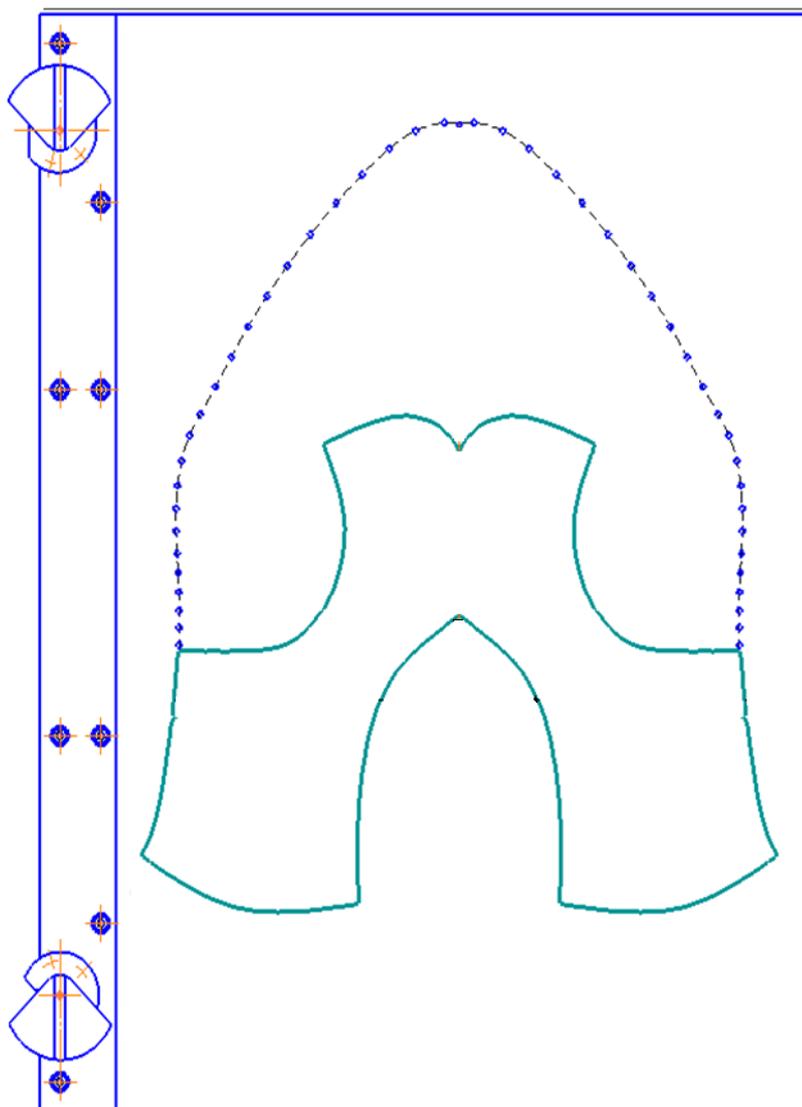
Конструкция кассеты для сборки заготовки верха обуви
